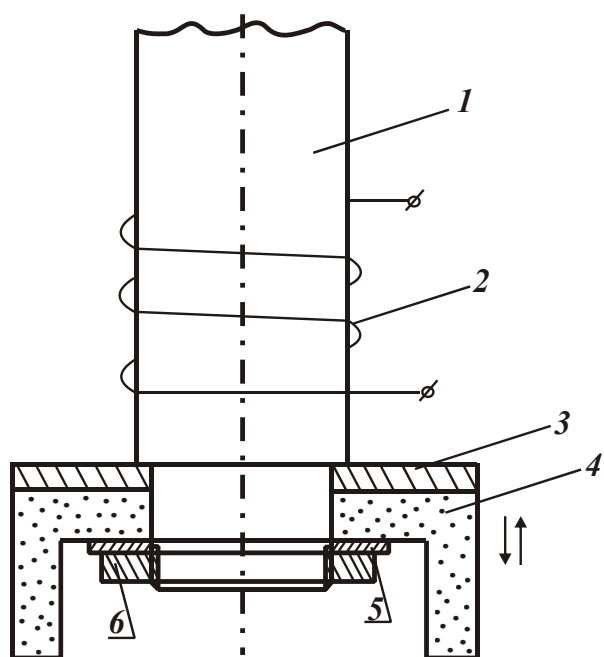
Устройство для шлифования с вибрациями: 1 – вал из магнитострикционного сплава; 2 – обмотка; 3 – упорная шайба; 4 – чашечный круг; 5 – прижимная шайба; 6 – гайка.
